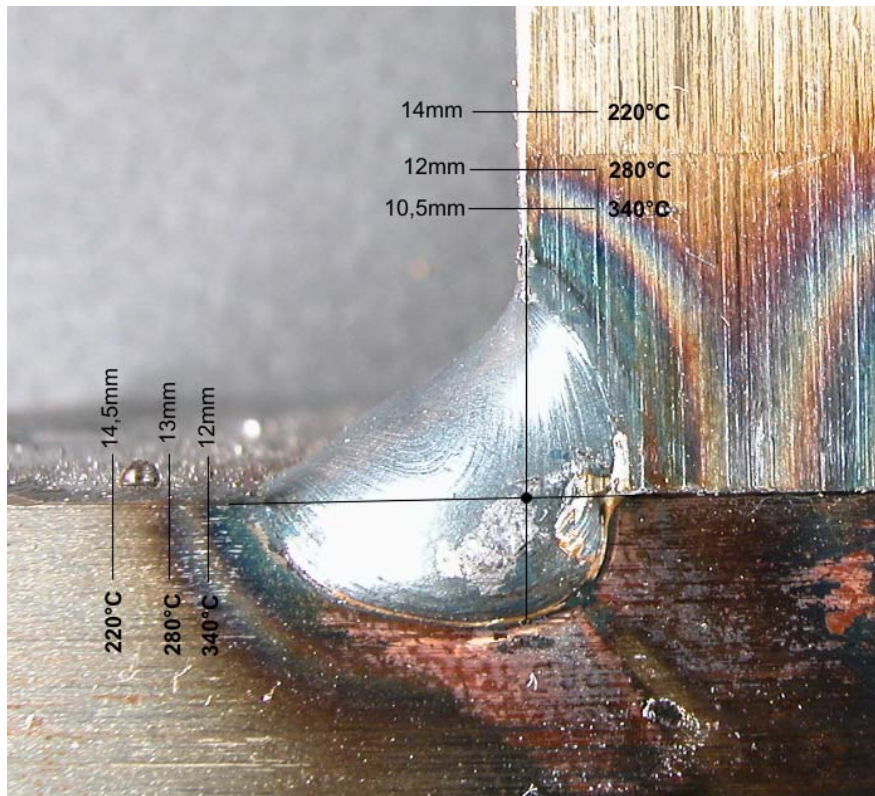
Schweißprobe mit Anlauffarben
